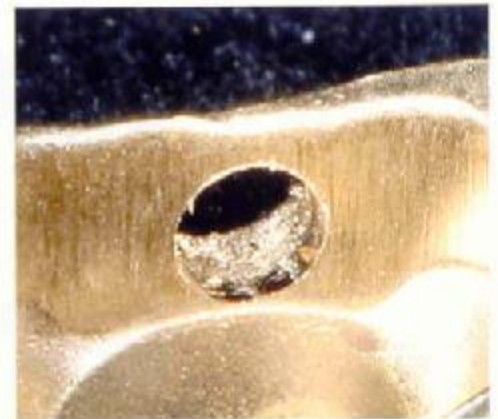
wie auch in der Innenansicht deutlich wird
